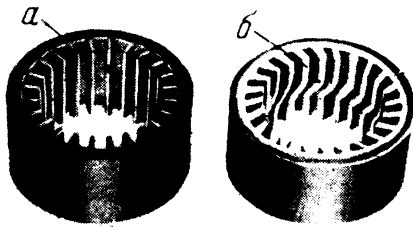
Прессованная заготовка коллекторных пластин.
